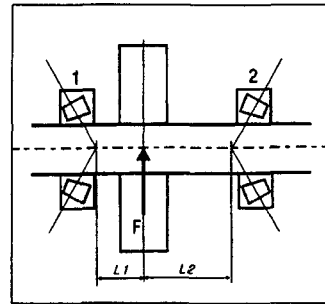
Axle Gear 베어링 배열(L1=29, L2=326)
